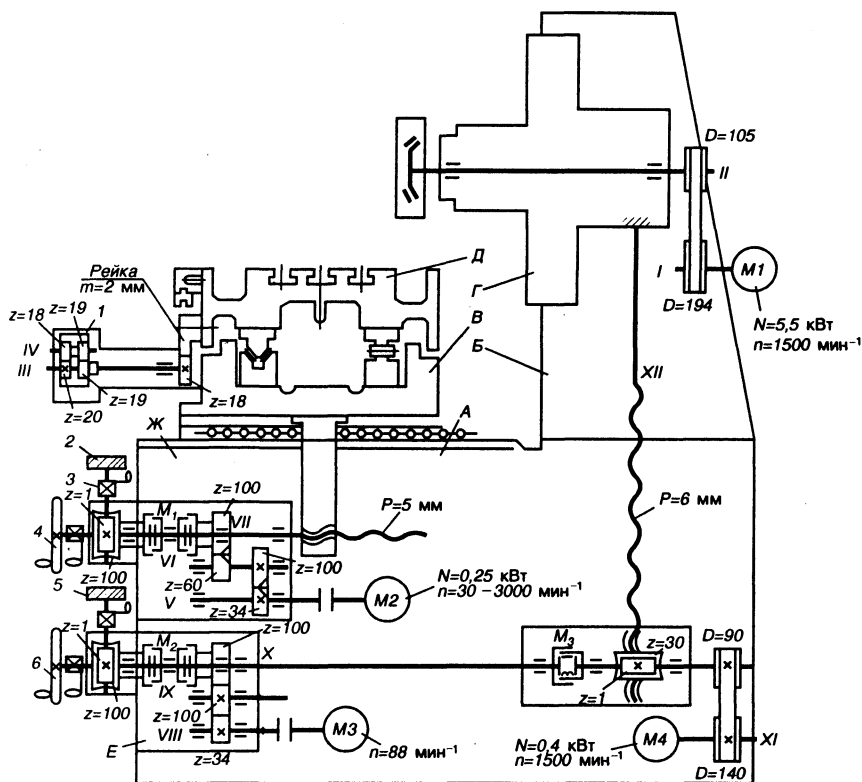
Кинематическая схема плоскошлифовального станка 3Е711В
